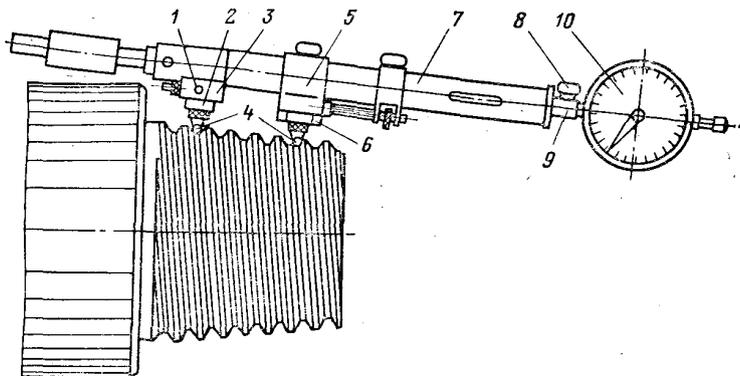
Схема проверки шага резьбы шагомером ШИ
